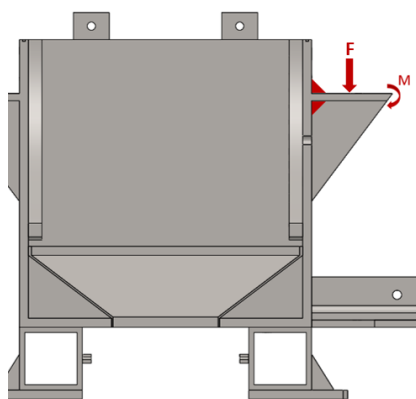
Zona soldada do suporte da chumaceira
